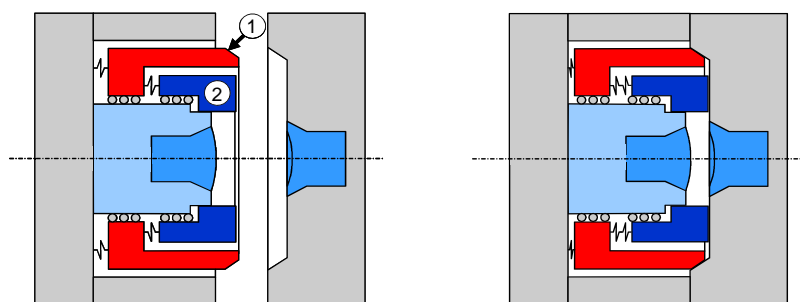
Schnitt durch das Spritzgießwerkzeug mit Prinzipskizze der Zentrierung
